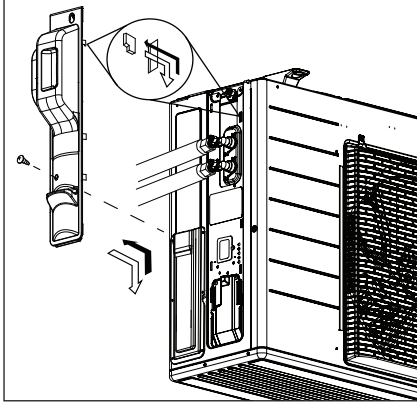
Retirer le couvercle principal pour accéder au deuxième couvercle.
